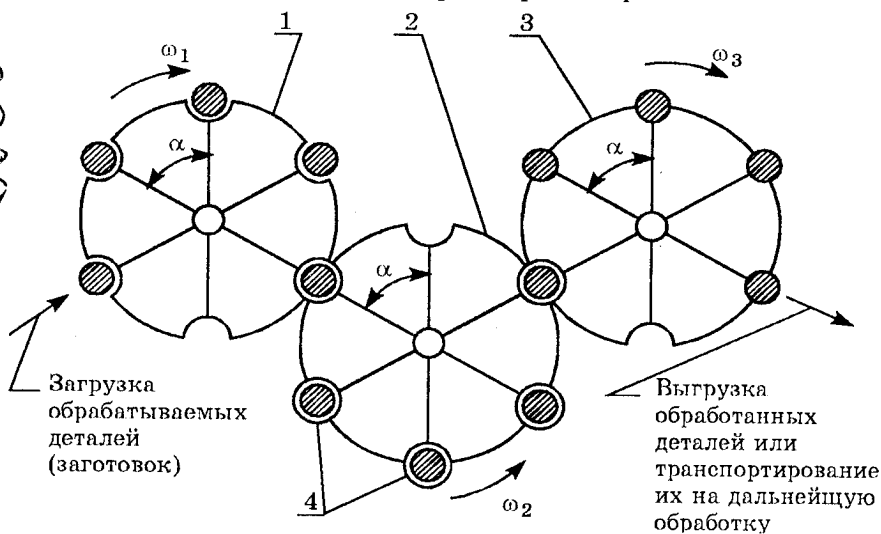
Схема РМА: 1,3 — транспортные роторы; 2 — инструментальный ротор; 4 — позиции обработки
